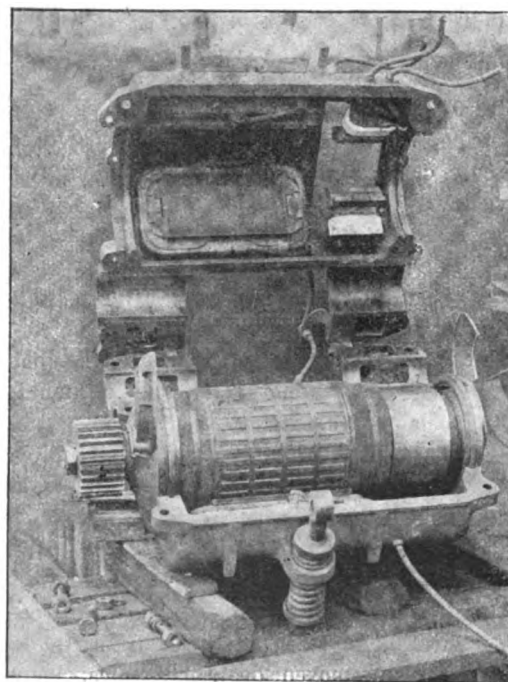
Moteur T. II. 4. Vue d'ensemble.
